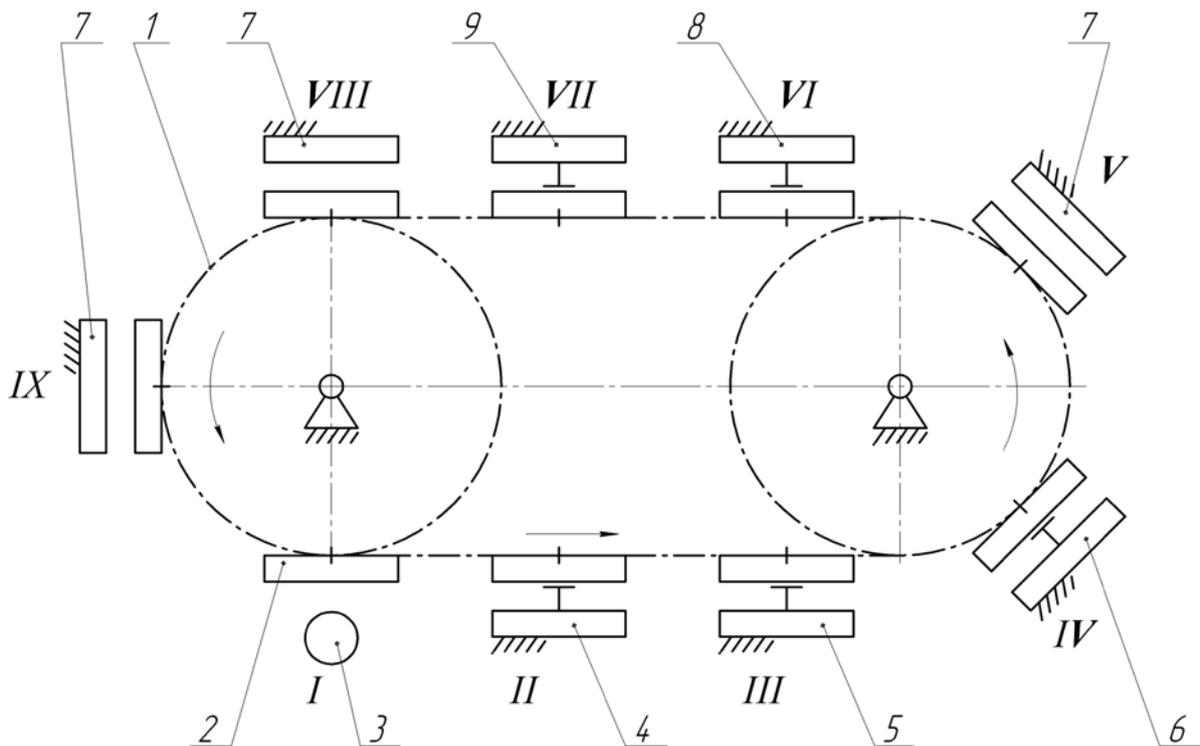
Технологическая схема агрегата контурной обработки подошв АКОВ-9: 1 – цепной транспортер, 2 – каретки (всего 9), 3 – оператор, 4, 5, 6, 8, 9 – обрабатывающие головки, 7 – установки для сушки (всего 3), позиции: I – загрузка-выгрузка, II – фрезерование контура подошв, III – увлажнение, IV – нанесение мыльной эмульсии, V – подсушка, VI – уплотнение, VII – покраска торца, VIII, IX – сушка
